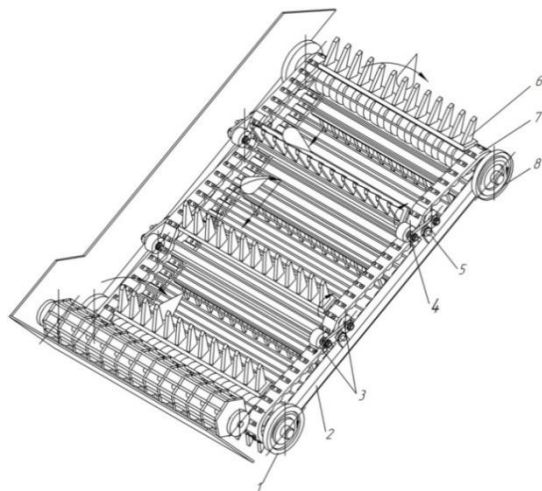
Конструктивна схема скребкового транспортера-доочисника коренеплодів
